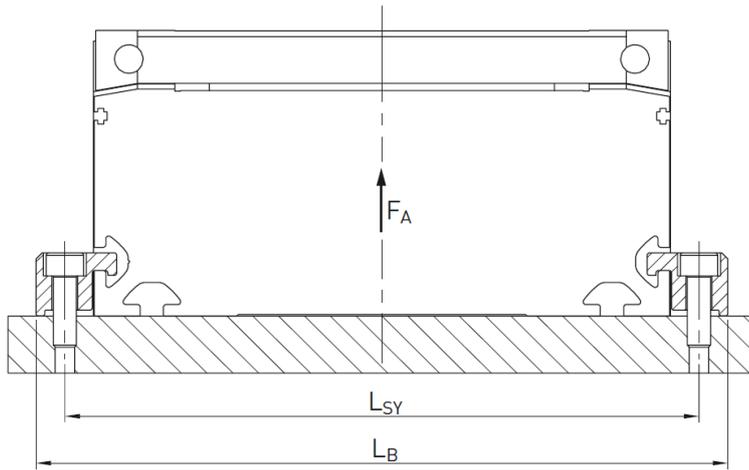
Befestigung mit Spannprofilen – HB-R
